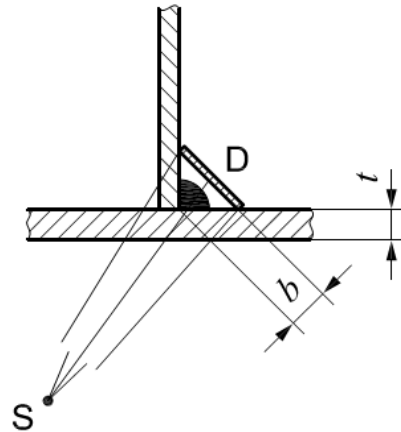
Схема контроля при просвечивании угловых сварных швов
